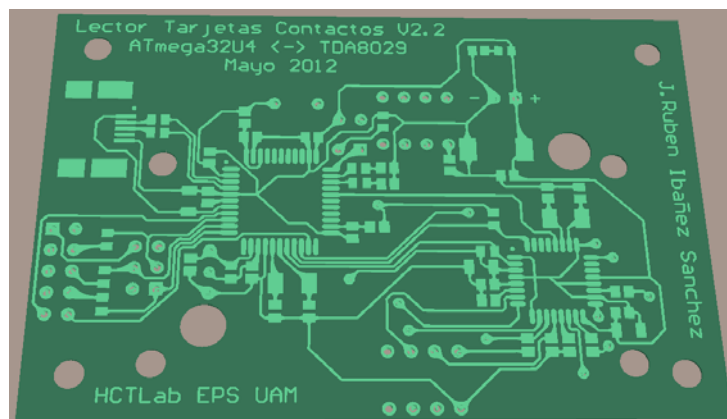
20: Vista 3D del PCB terminado sin componentes.
